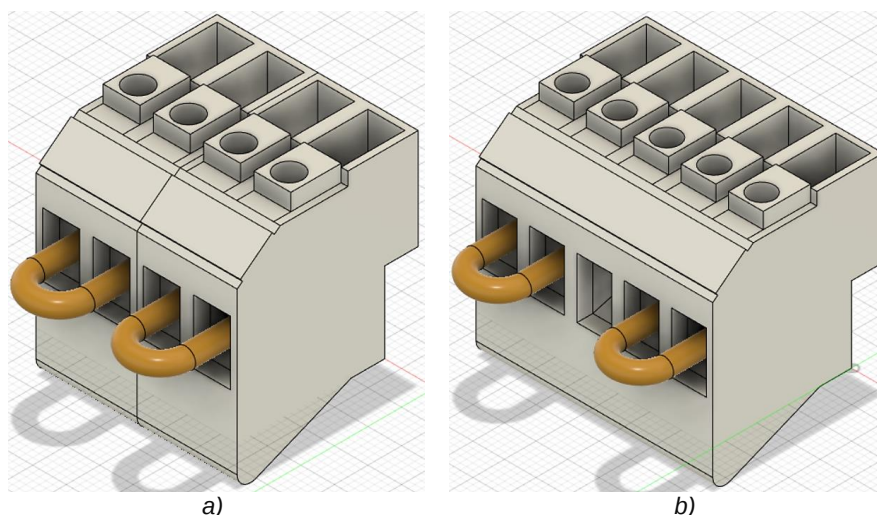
a) clema estrecha y b) ancha - Fuente: El autor
